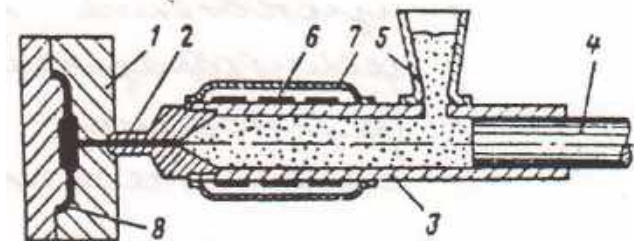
Схема лиття під тиском: 1 – прес-форма; 2 – сопло; 3 – приймальна камера; 4 – плунжер; 5 – бункер; 6 – нагрівач; 7 – кожух; 8 – готова деталь
